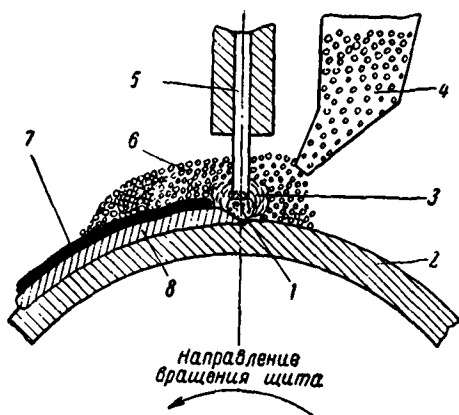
Схема процесса плавнения электродной проволоки при автоматической наплавке под слоем флюса:
